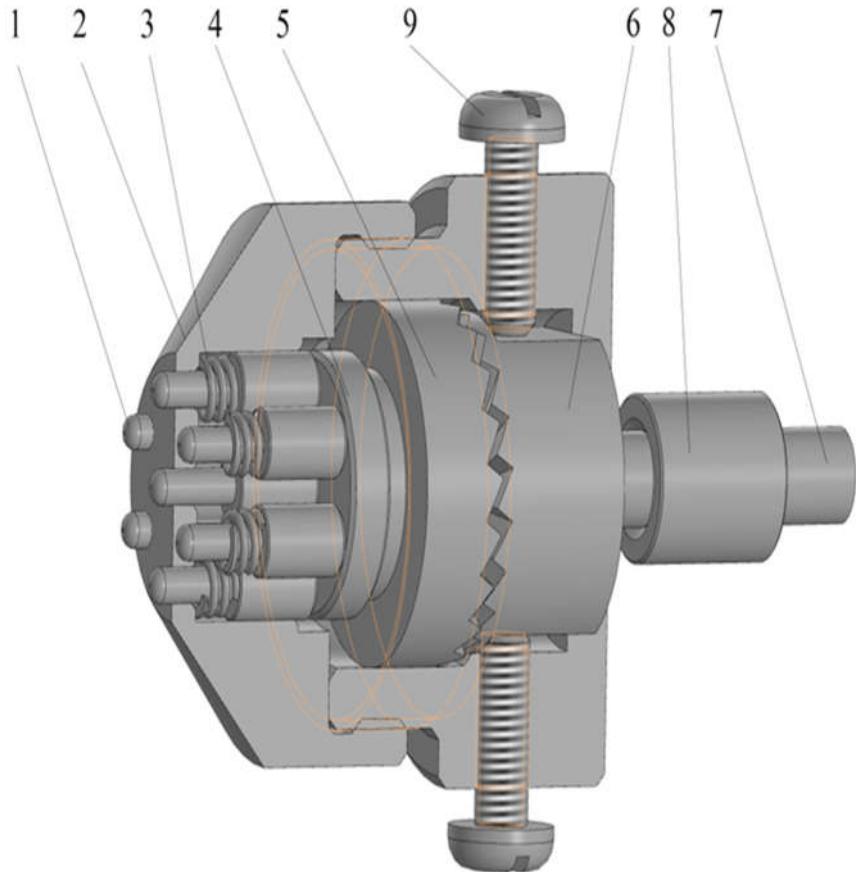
Схема устройства для поверхностно-пластического упрочнения:
